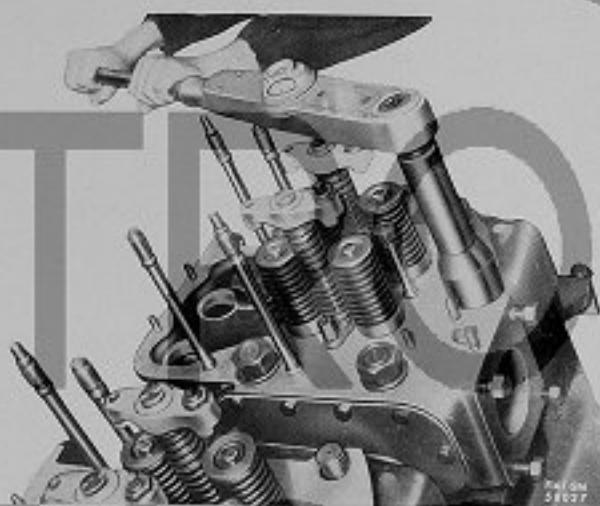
Testata cilindro del motore 2312 SF in fase di montaggio.
